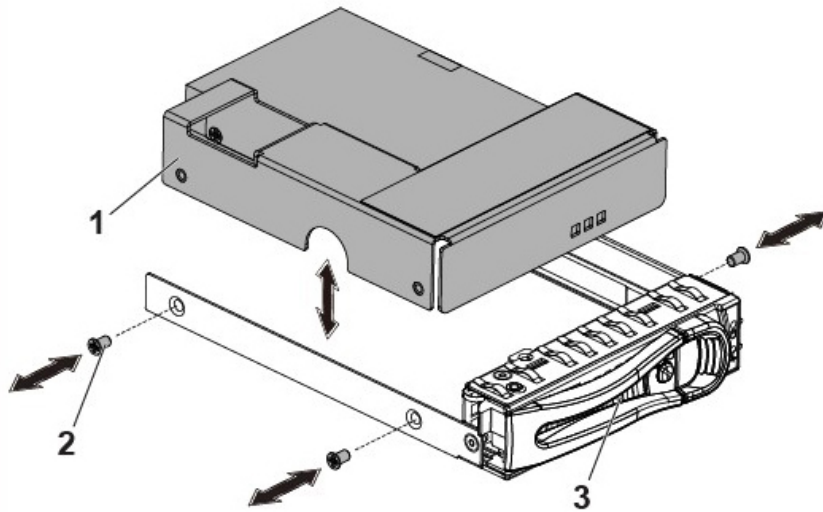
Retrait et installation d'un assemblage d'adaptateur du support de disque dur
